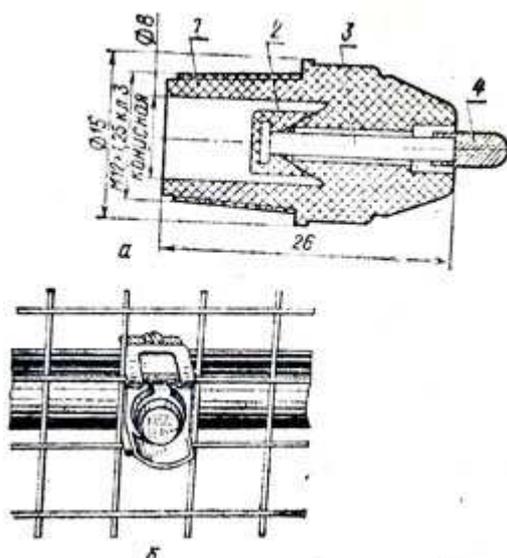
Автоматические поилки для норок: А - схема ниппельной автопоилки; Б - общий вид автопоилки; 1 - корпус ниппеля; 2 - клапан; 3 - шток ниппеля; 4 - наконечник штока
